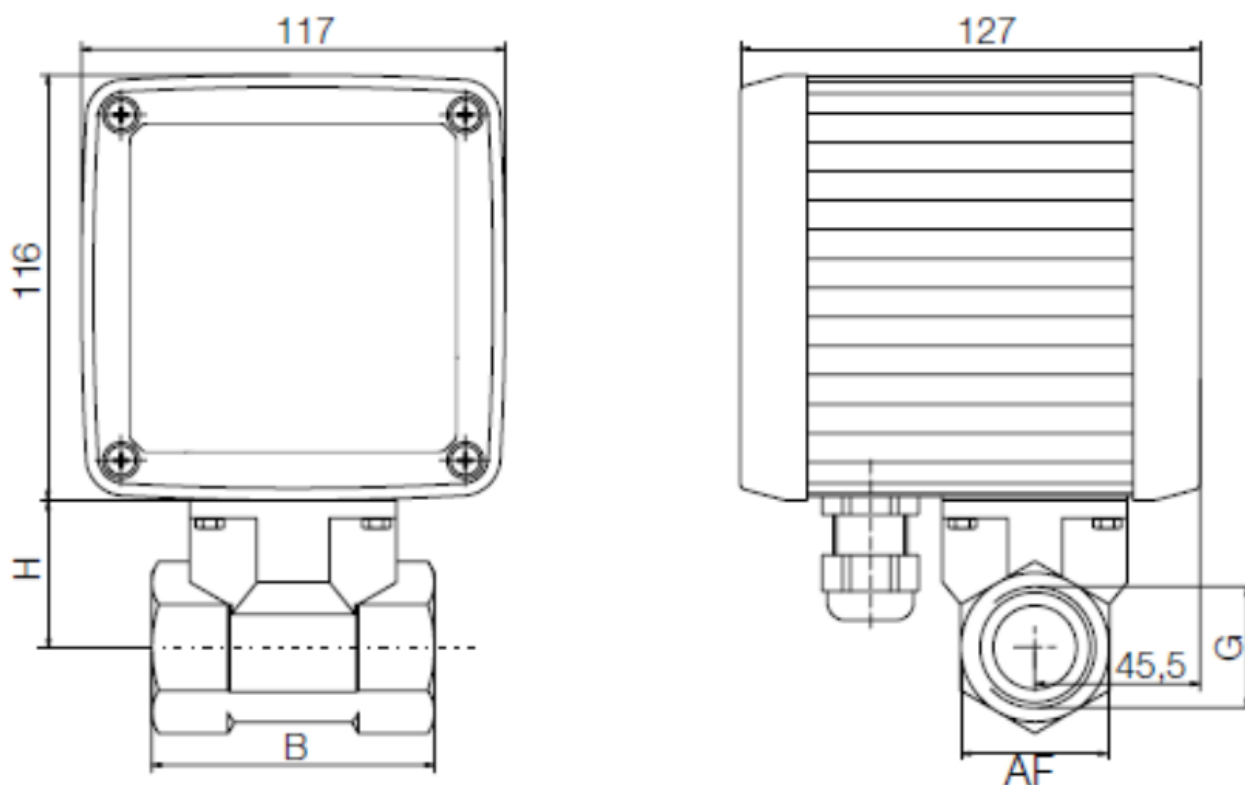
Габарити лічильника KOBOLD DPE.
